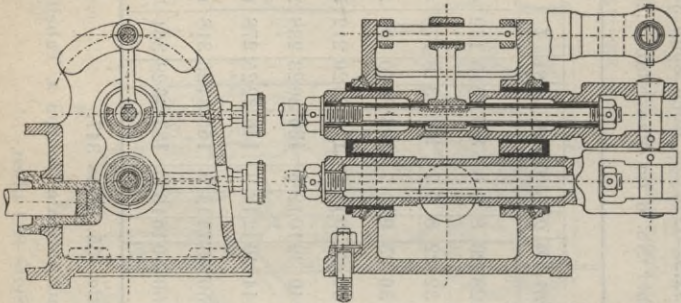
Führungsstücke aus Gusseisen oder Stahlguss.\*)
